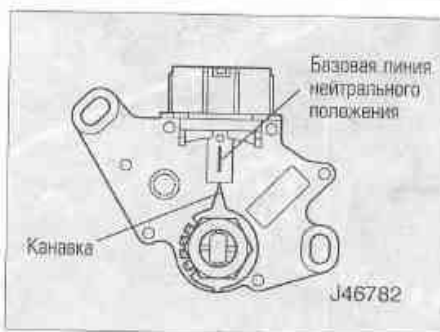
Поверните переключатель настолько, чтобы базовая линия нейтрального положения совместилась с канавкой, и затяните болты
